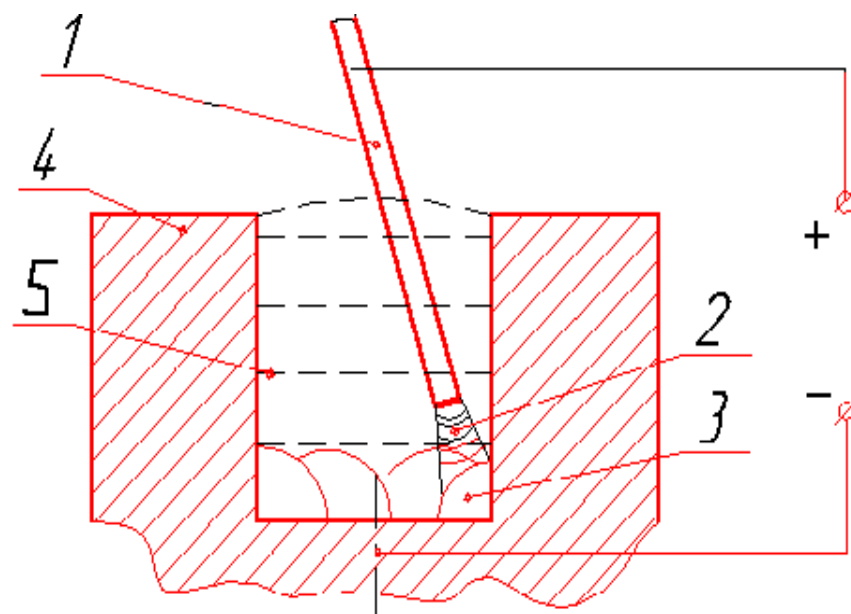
Схема багат шарового наплавлення нижнього ковочного
